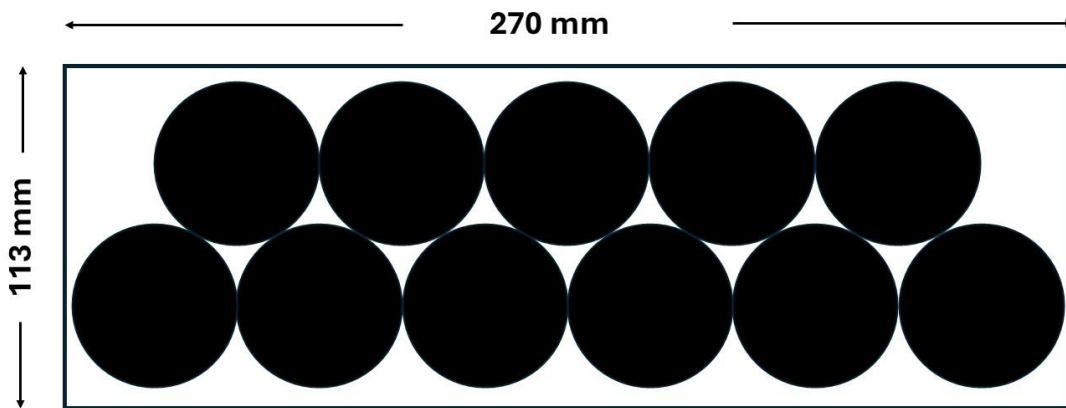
Vista de planta de la caja de cementación. Cotas en mm.
